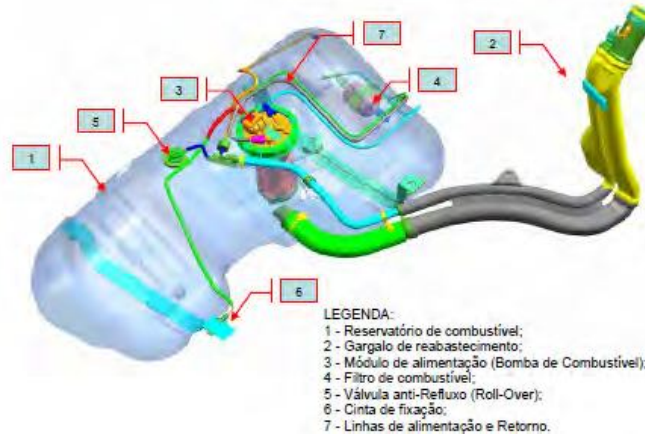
Tanque de Combustível e seus Componentes Básicos.
